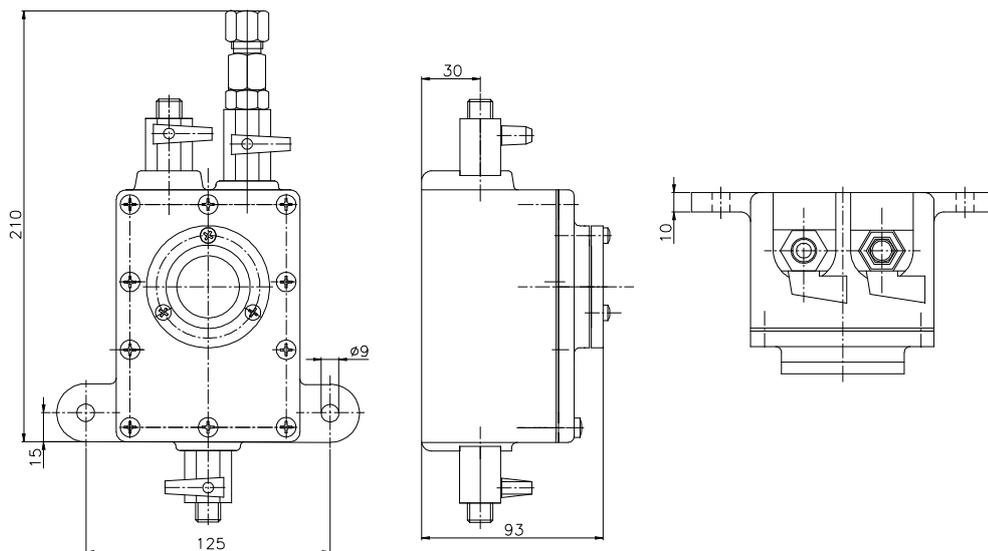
Размерный эскиз газоотборного устройства ZG 1.2.
